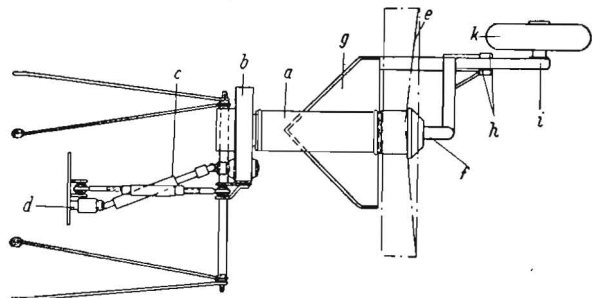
Schleuderradroder für Schlepperbetrieb (Draufsicht)
